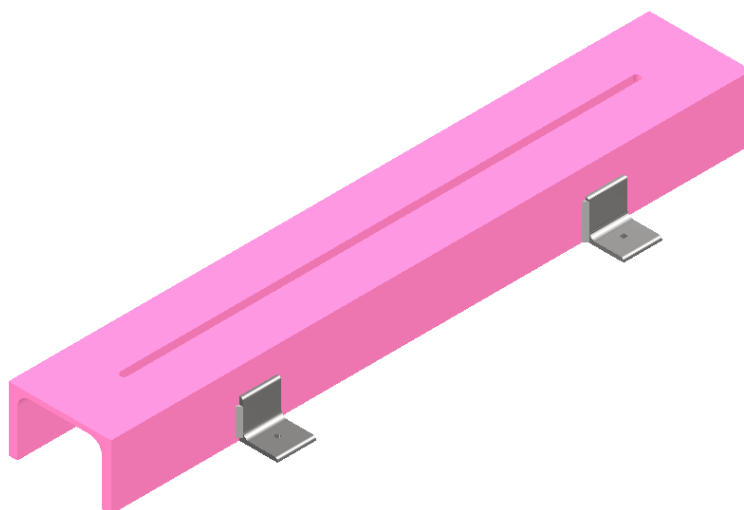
Náhled na hotovou sestavu konstrukčního řešení
